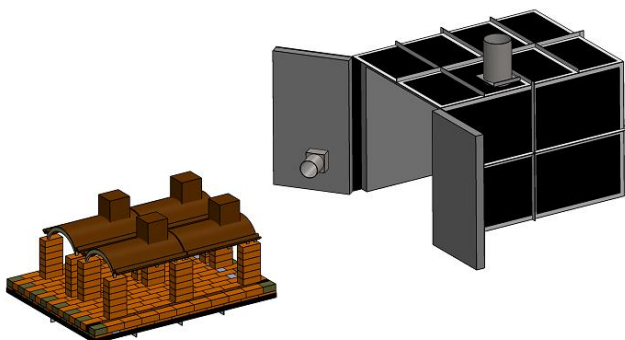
Vista Explosionada del horno y Base con bóvedas de puerto
